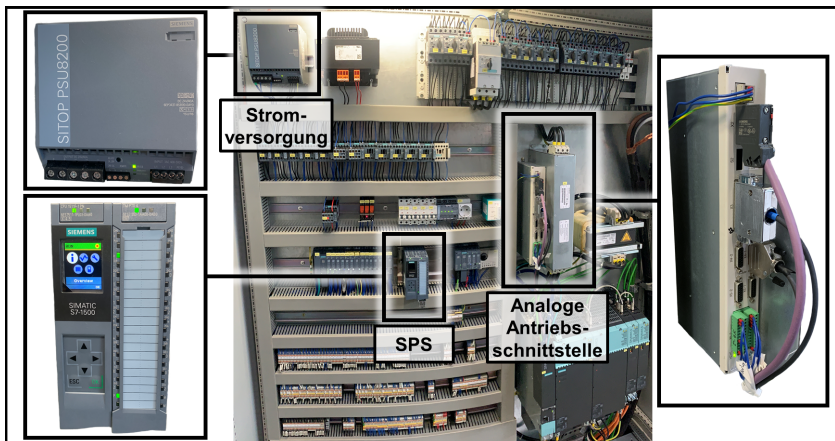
Steuerungsbezogene Komponenten zum Betrieb des Werkzeugsystems auf einer Werkzeugmaschine
